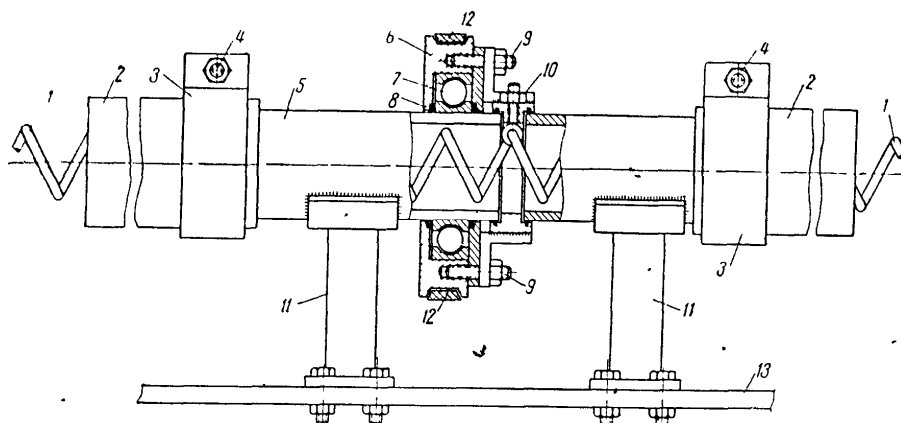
Деталь крепления спирали при двусторонней работе установки
